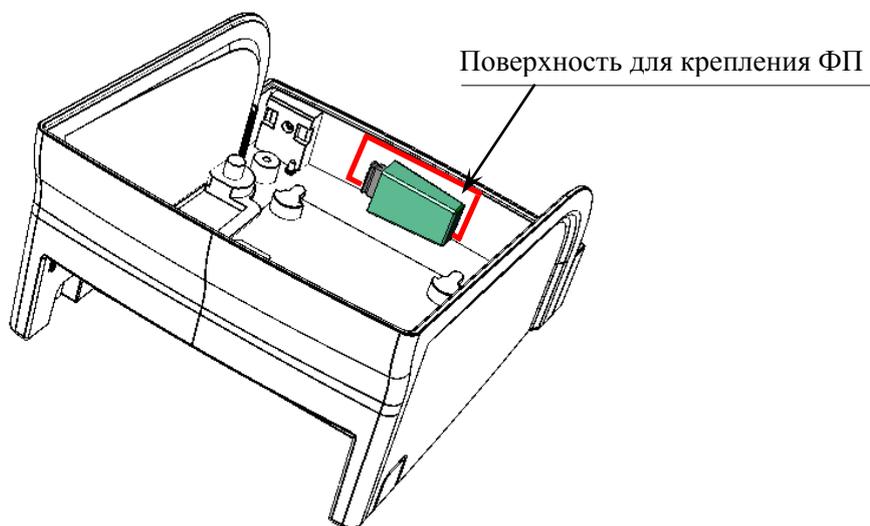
Поверхность для крепления ФП в корпусе изделия
